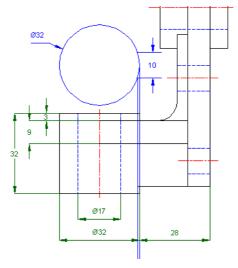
Zoom sur la construction géométrique d'un point particulier
